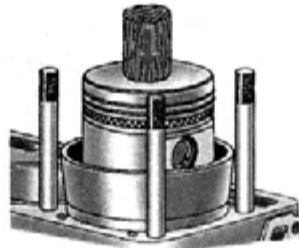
Установка поршня с кольцами в цилиндр с помощью приспособления 5-У-11106
